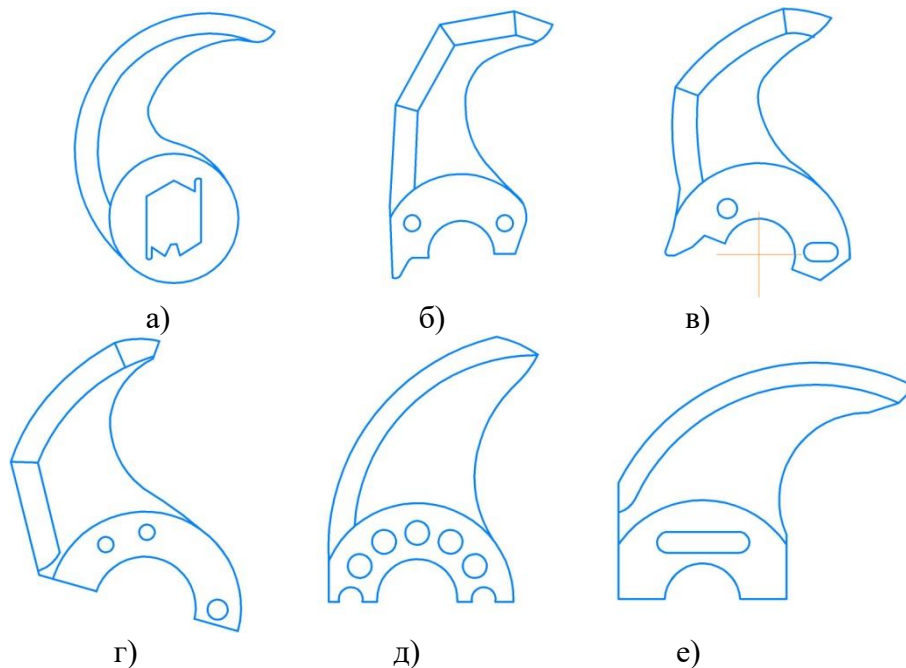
Схеми конструкцій ножів: а) – Seydelmann; б) – Laska I; в) - Laska II; г) - Kilia; д) - Alpina; е) - Л5-ФКБ
